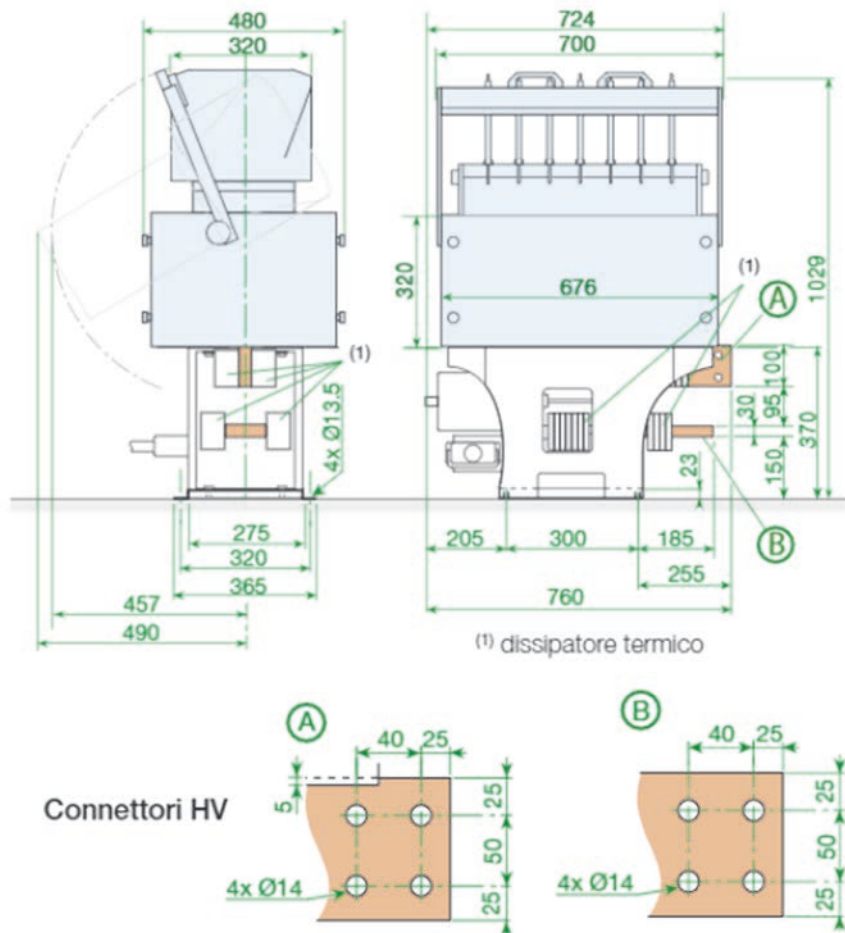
Esempio del disegno tecnico dell'interruttore extrarapido.
